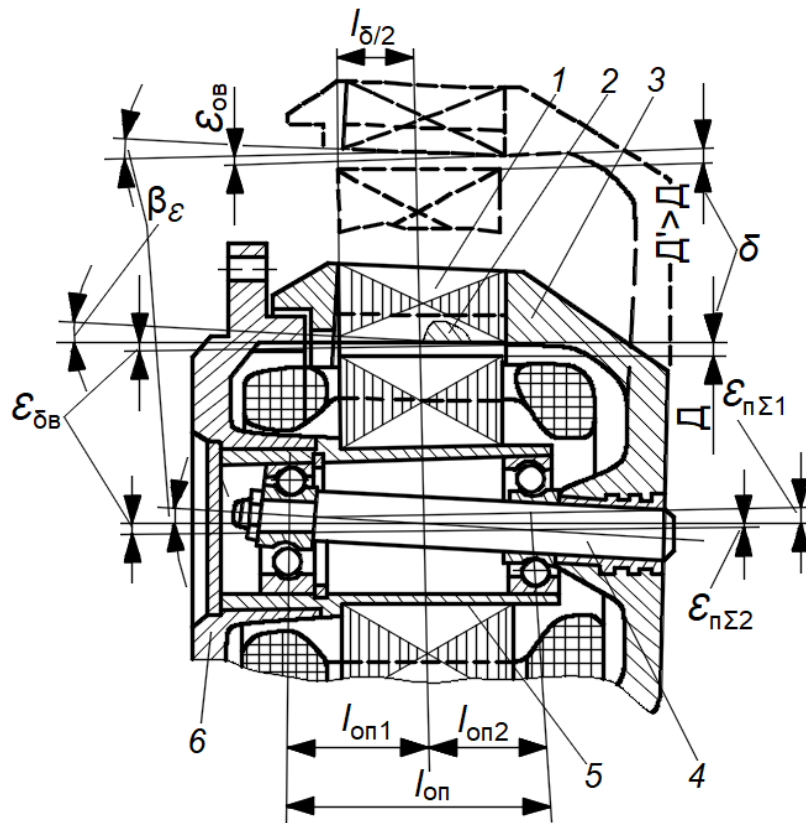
Конструктивна схема та ексцентриситет зазору АДВР із чешевидним ротором консольної установки: 1 – ротор; 2 – короткозамкнена клітина; 3 – корпус ротора; 4 – вал; 5 – маточина; 6 – корпус статора.
